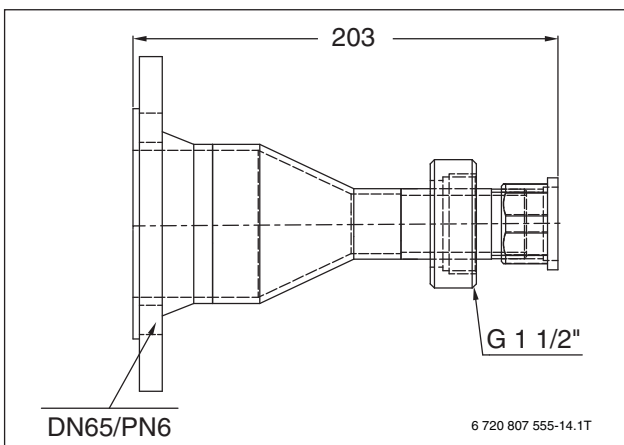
Anschlussstück DN 65/PN 6 – G 1 1/2" (Maße in mm)
